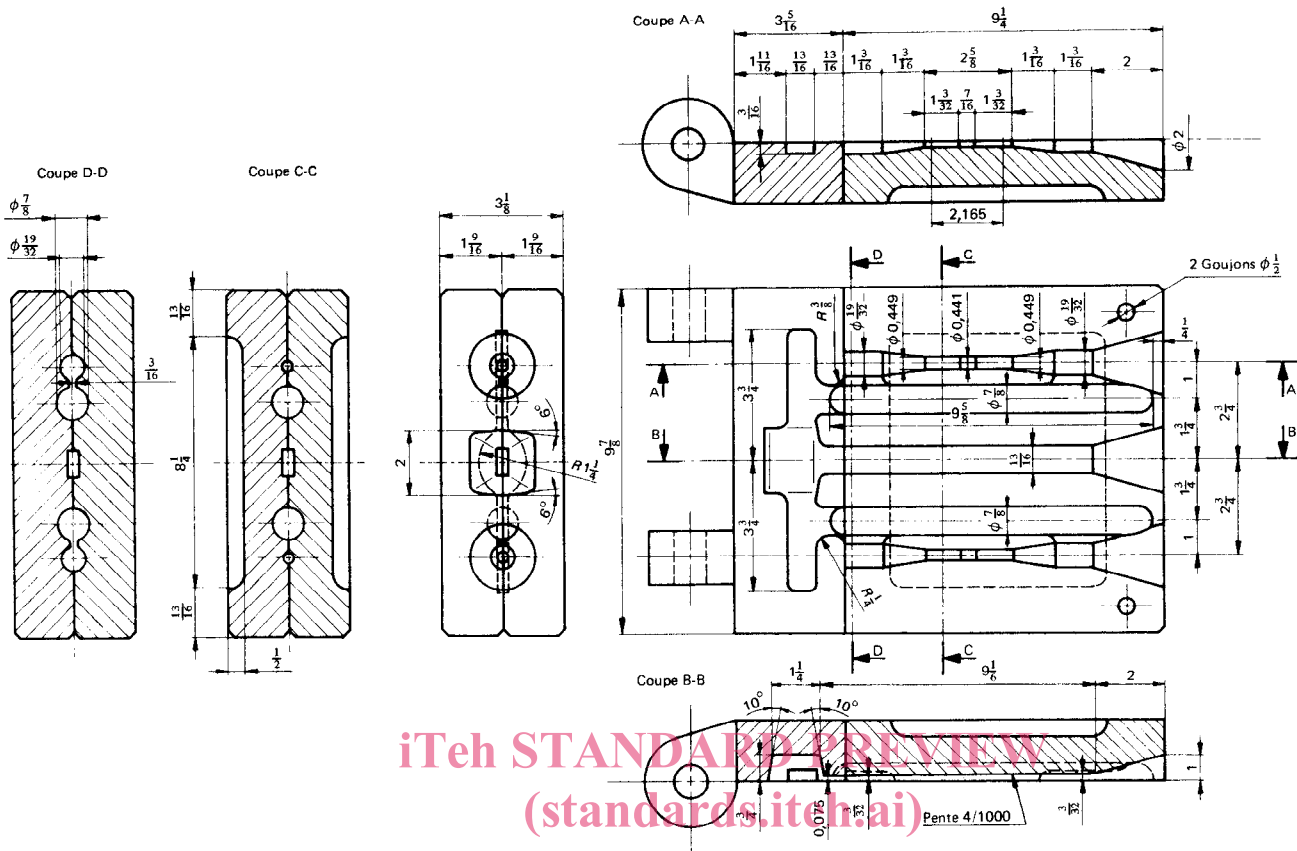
Coquille pour éprouvettes de référence – Dimensions en millimètres
